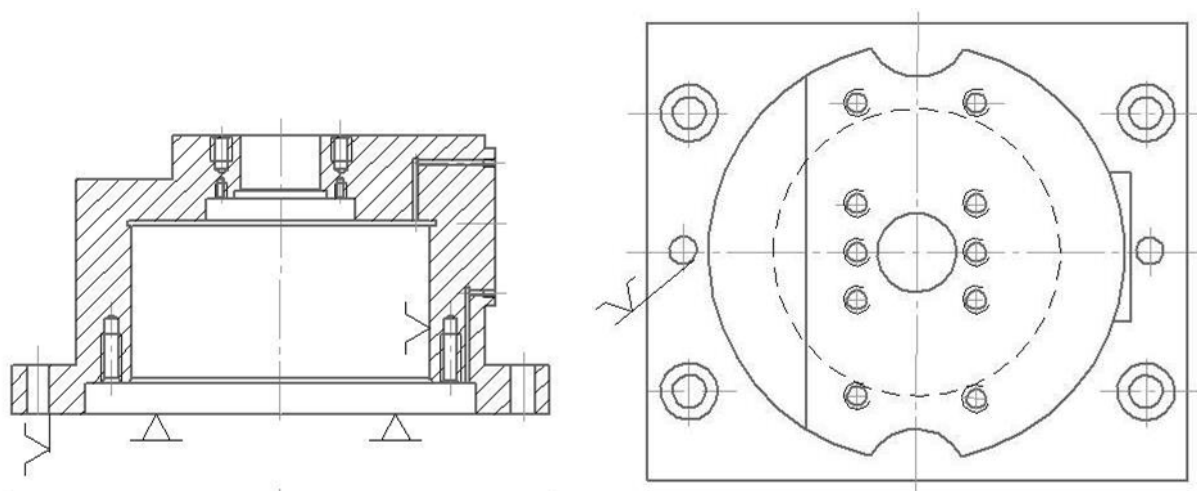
Схема базування заготовки деталі «Корпус» (I-042.8.H72.00)
